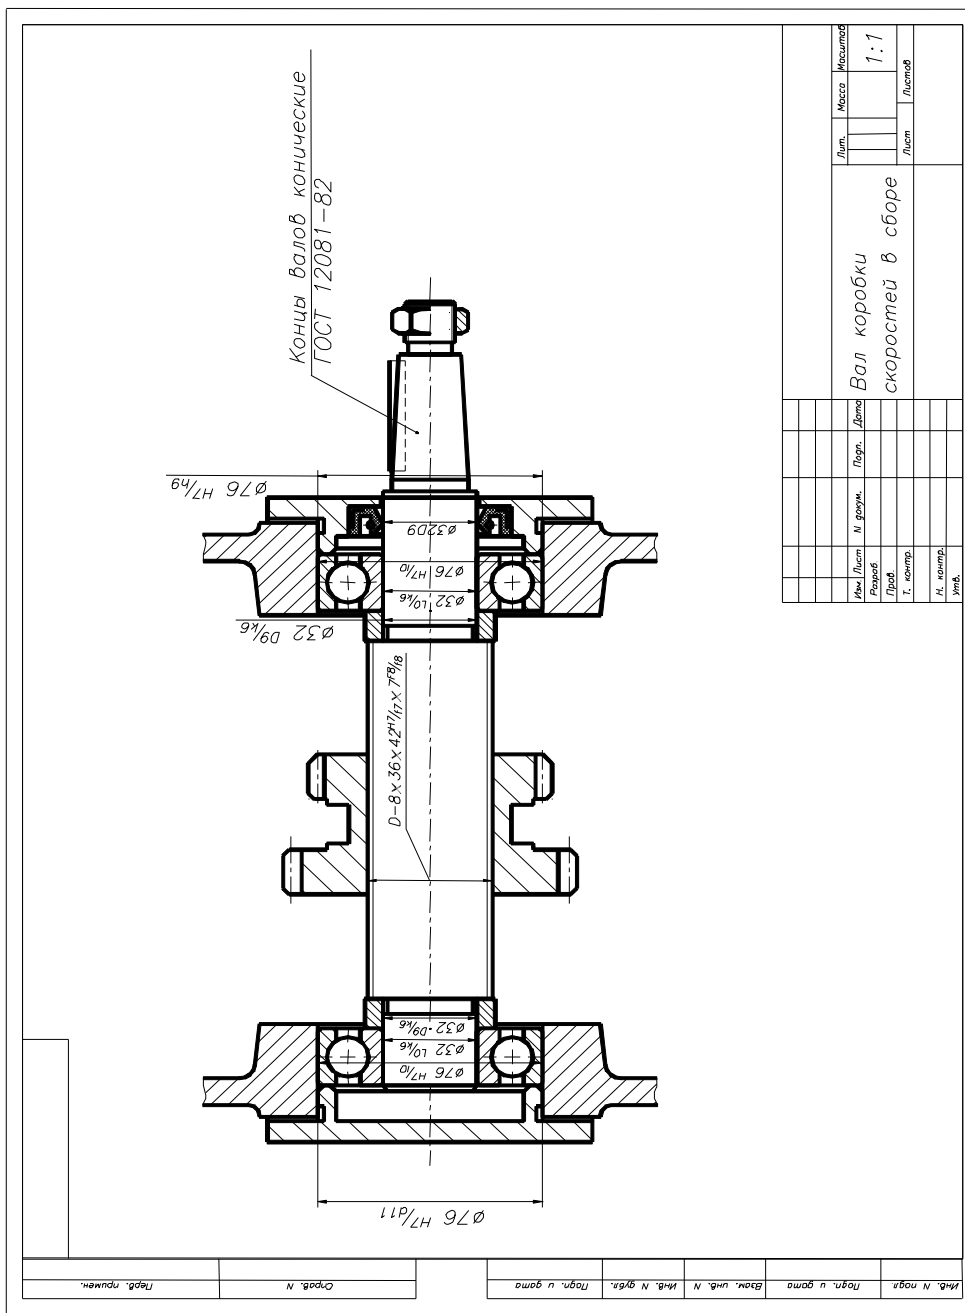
Рабочий чертеж узла вала коробки скоростей
